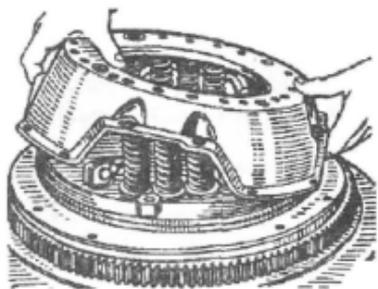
Зняття кожуха натискного диска зчеплення
